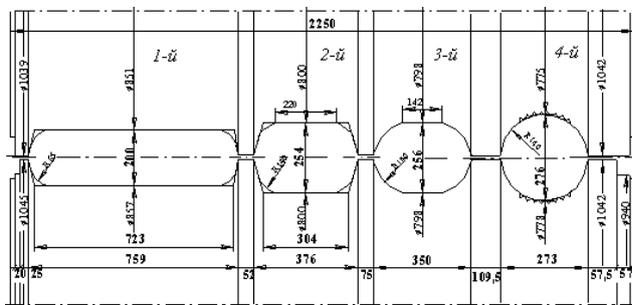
Калибровка валков для прокатки круга диаметром 265мм
